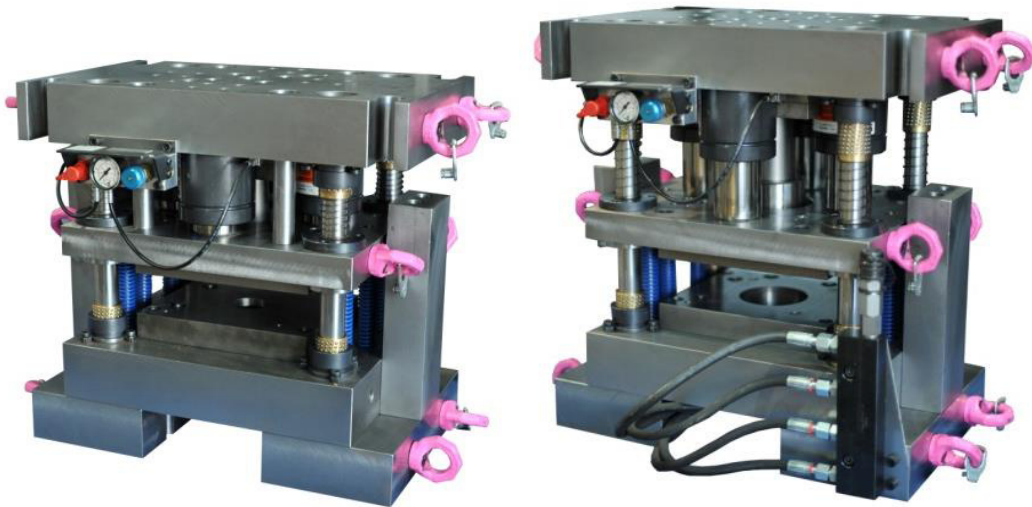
Scherschneidwerkzeug (links) und Kragenziehwerkzeug (rechts)
